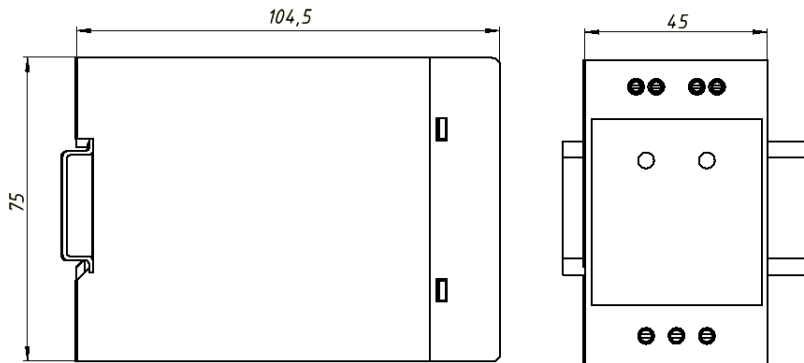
Габаритные размеры блока питания PSM-2/3-24
